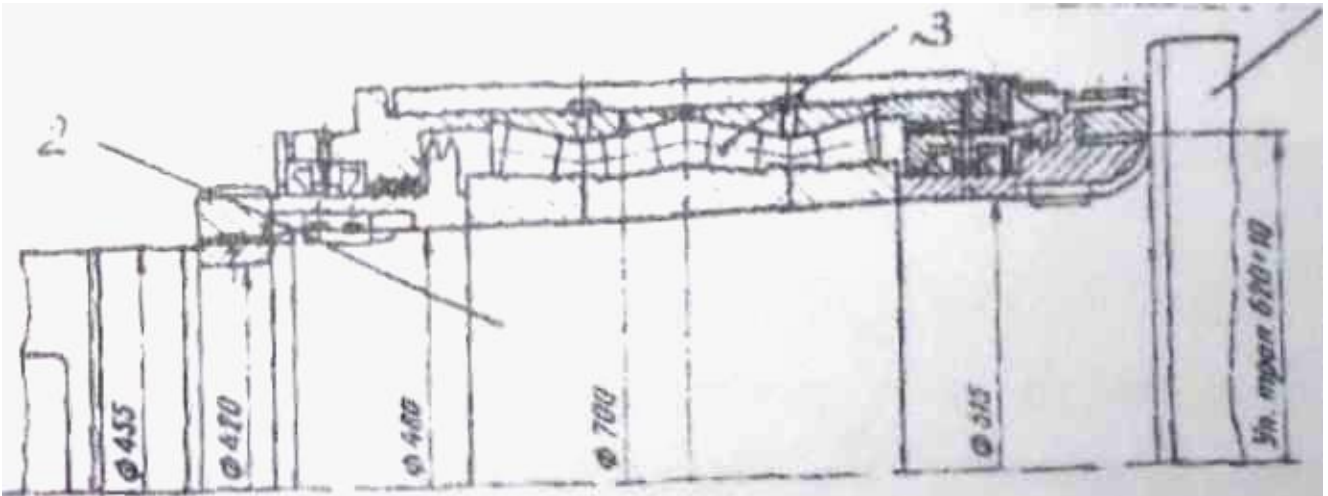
Установка конічного роликпідшипішка на конічній шийці валка кліті кварто 2000:1 -бочка, 2 -шийка, 3 -підшипник.
